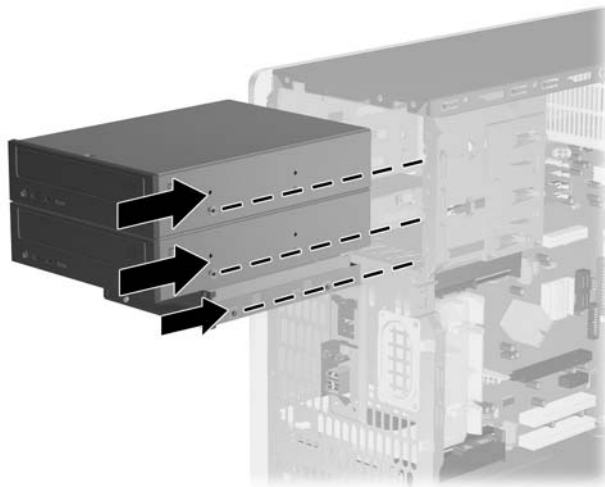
Installieren von Führungsschrauben (am optischen Laufwerk)
